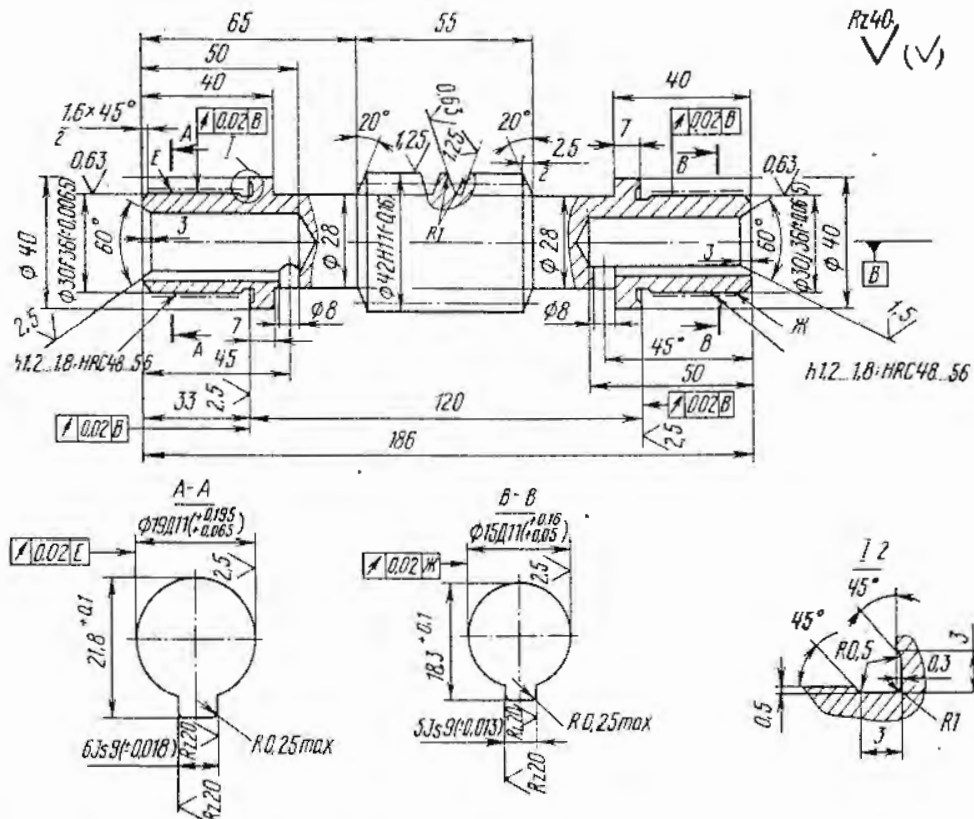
Червяк, деталь № ЗЛ722А.166.401 НВ 229...285
